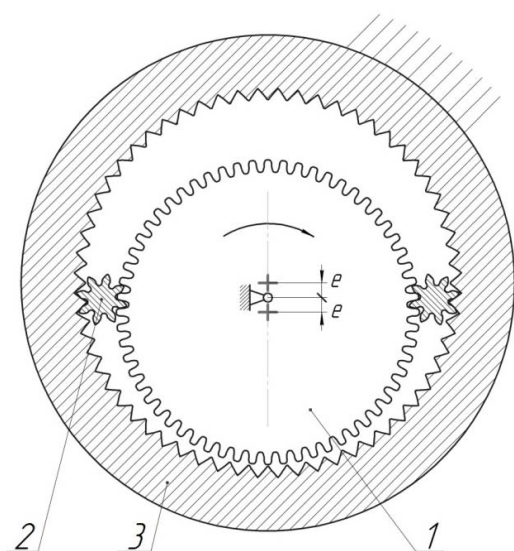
Планетарно-роторная гидромашина: 1 – центральное колесо с внешним зацеплением; 2 – центральное колесо с внутренним зацеплением; 3 – плавающие сателлиты
